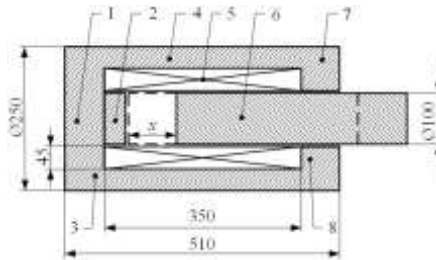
Схема базовой модели линейного двигателя: 1 – торцевой упор нижнего ярма статора; 2 – торцевой упор; 3 – нижнее ярмо статора; 4 – корпус статора; 5 – катушка; 6 – якорь; 7 – верхнее ярмо статора; 8 – торцевой элемент верхнего ярма статора.
